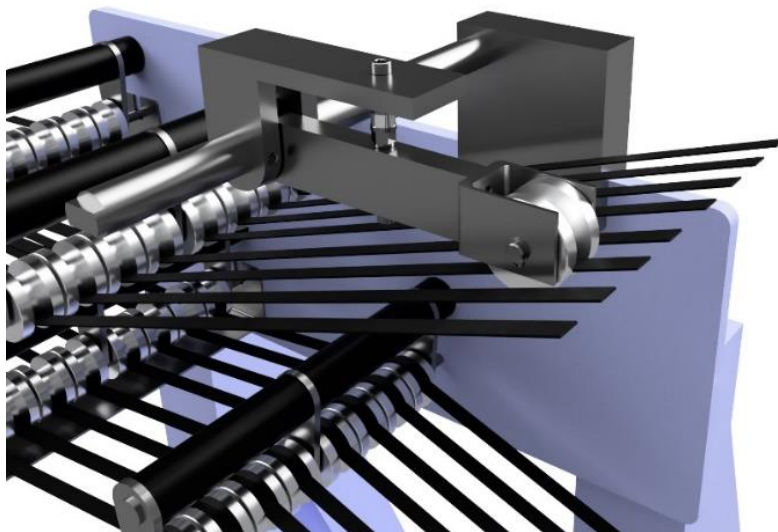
Assemblagem do protótipo final na cap-strip.
